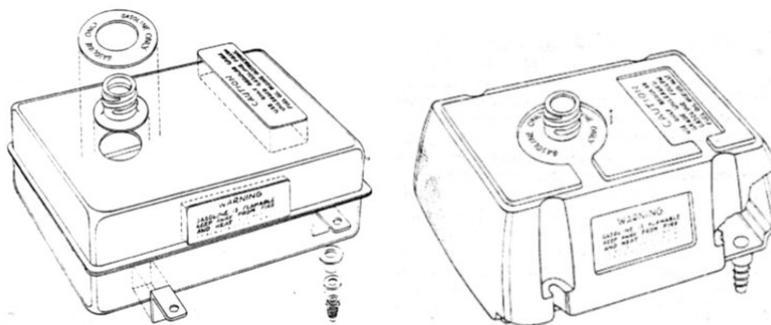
Tanque metálico original (à esquerda) e o projeto orientado à rotomoldagem (à direita).
